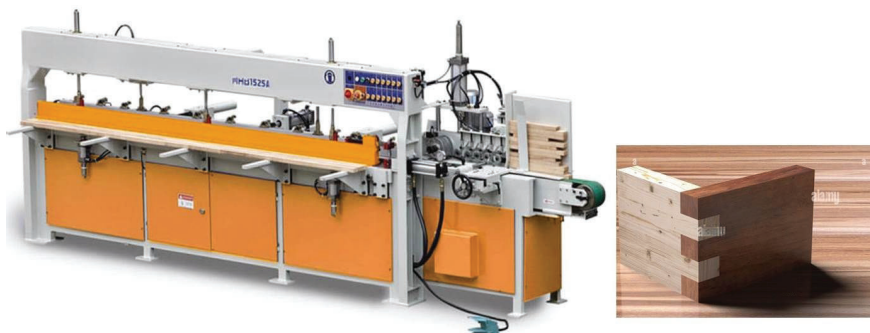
Автоматична лінія фрезерування шипових («finger joint»)
